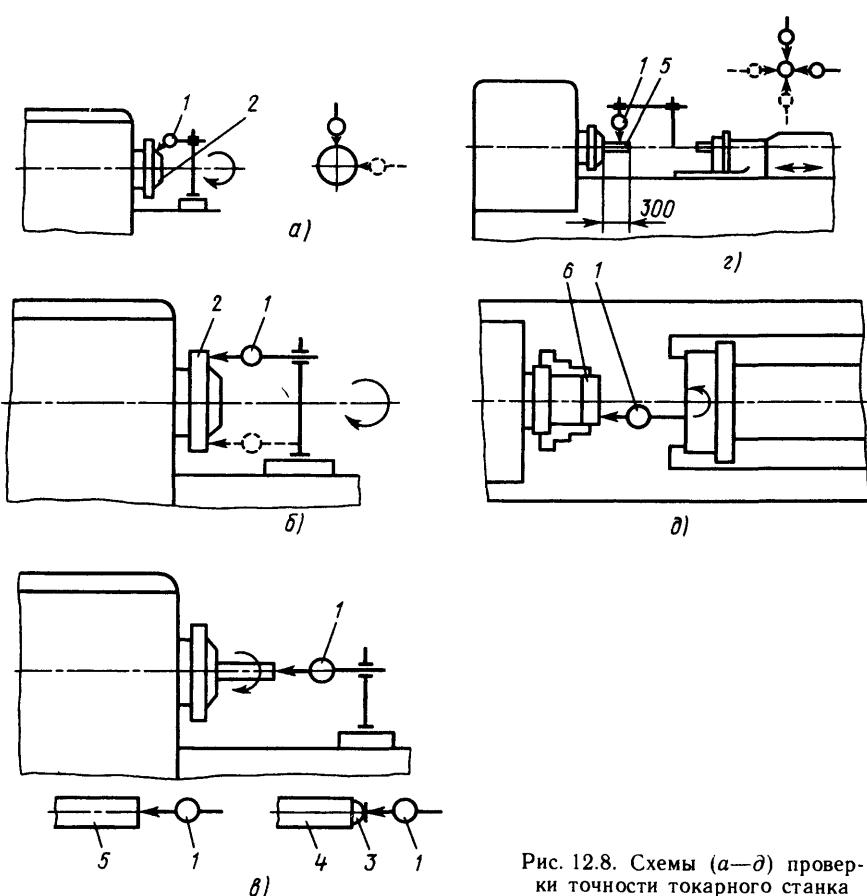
Схемы (а—д) проверки точности токарного станка
